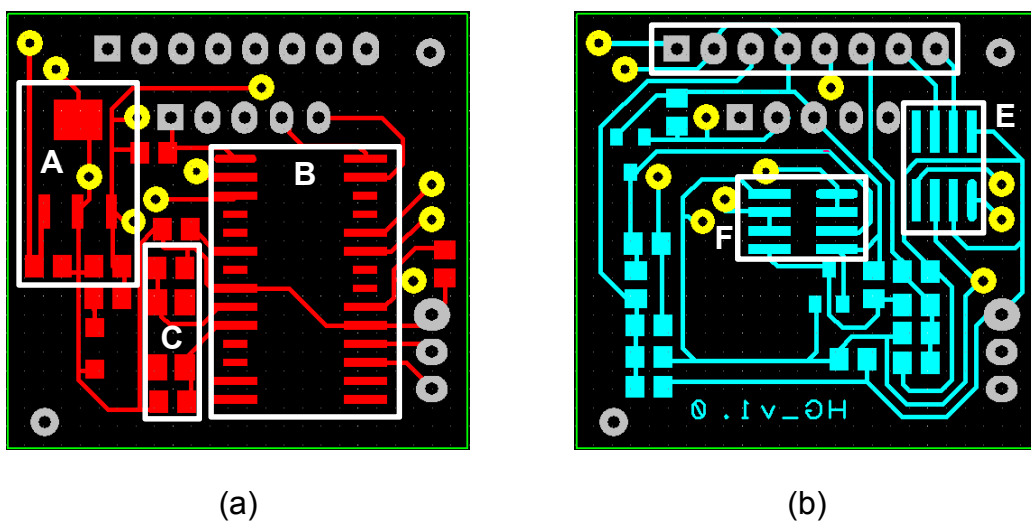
PCB do módulo de aquisição de sensores: (a) top layer e (b) bottom layer.
